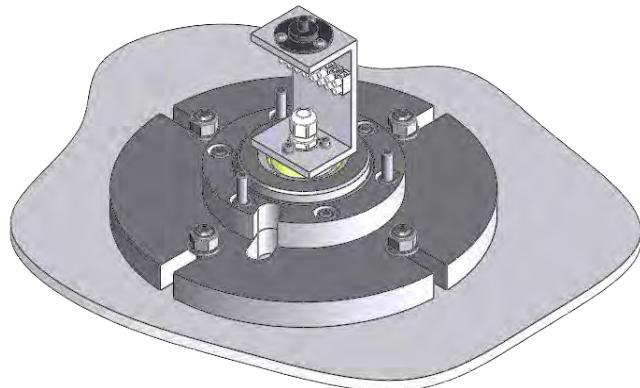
Корпус подшипника, установленного на крепежном кольце
